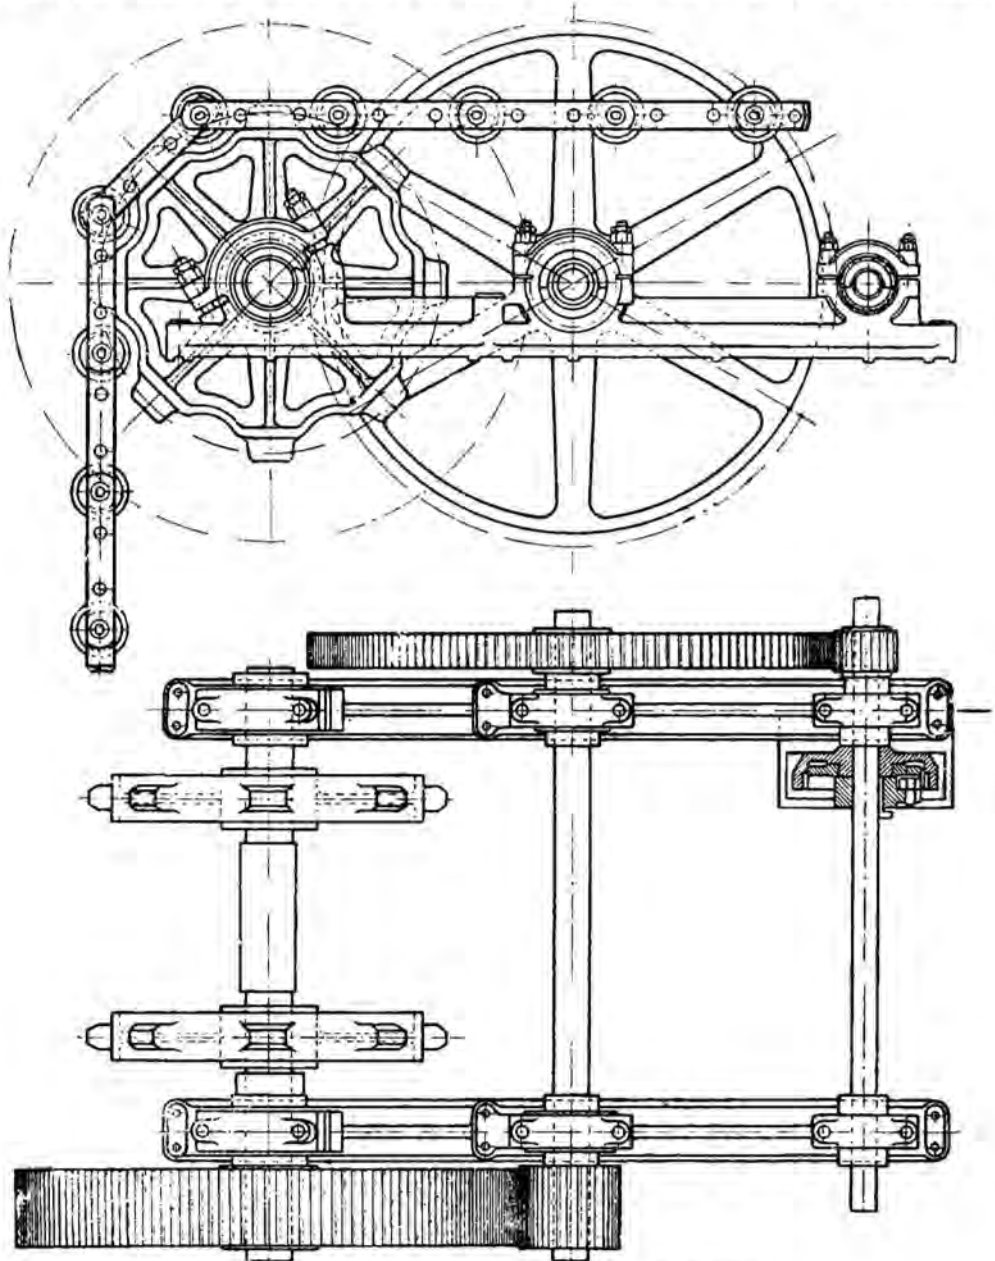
Схема привода цепного транспортера Pohlrig.
